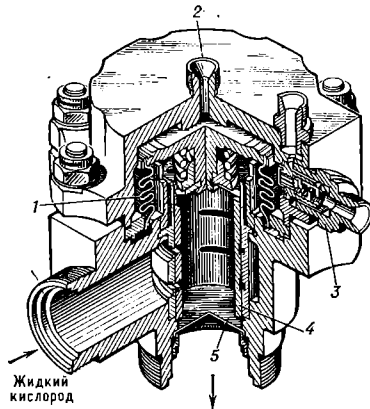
Редуктор давления с мембраной свободного прорыва для газогенератора ЖРД РД-111: 1 — разделительный сиффон; 2 — штуцер подачи управляющего воздуха; 3 — травящее устройство; 4 — золотник; 5 — мембрана свободного прорыва
